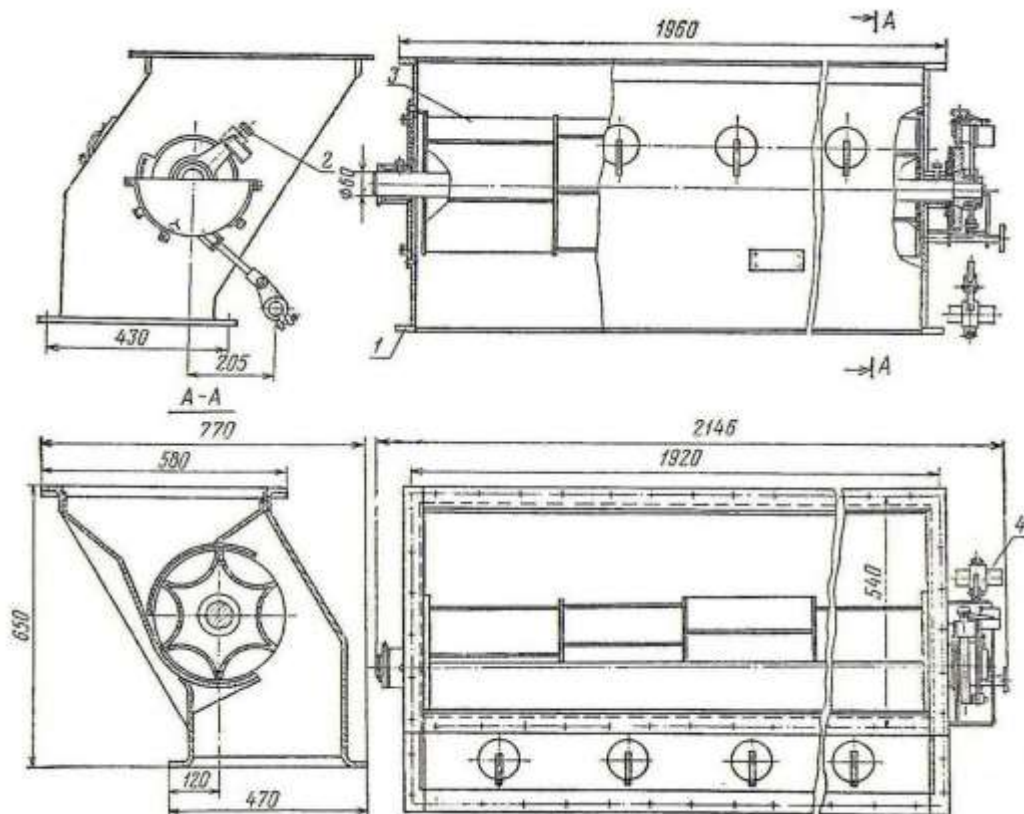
Дозатор ДМ-3А: 1 – корпус; 2 – регулятор подачі; 3 – дозуючий барабан; 4 – привідний механізм.
